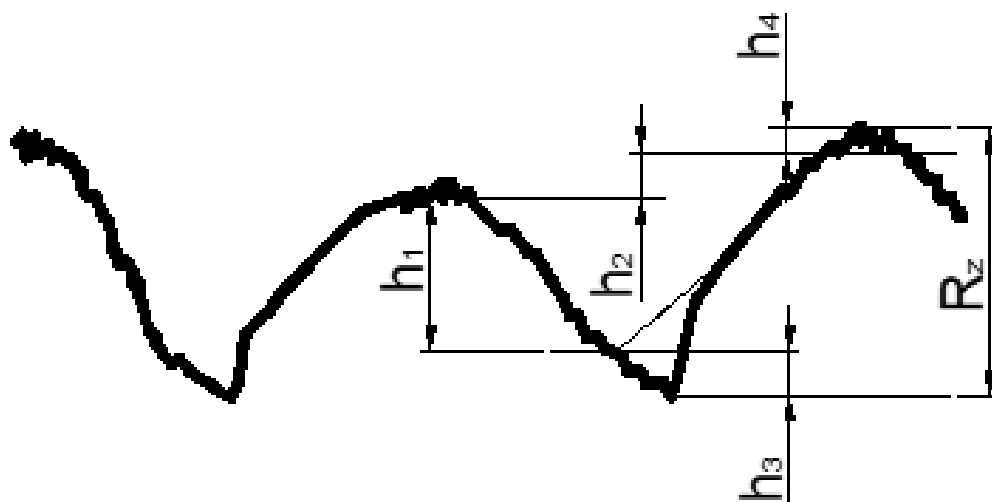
Схема для расчета высоты профиля шероховатости поверхности при точении:  $h_1, h_2, h_3, h_4$  – составляющие шероховатости [2]
